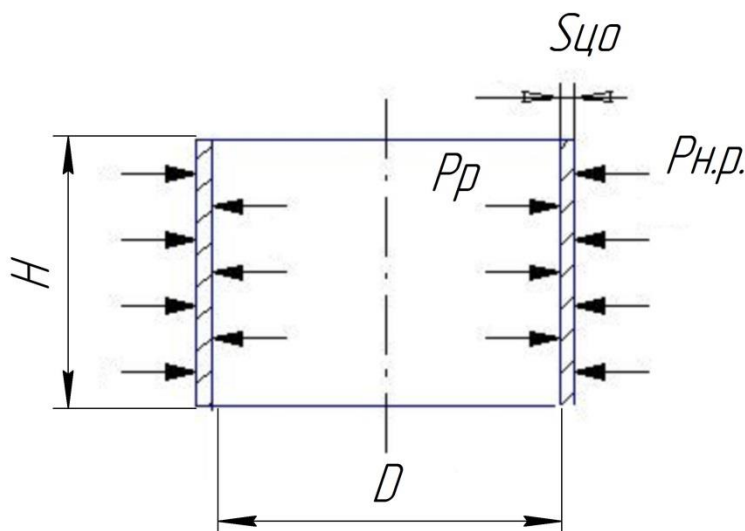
Расчётная схема цилиндрической обечайки (1)
